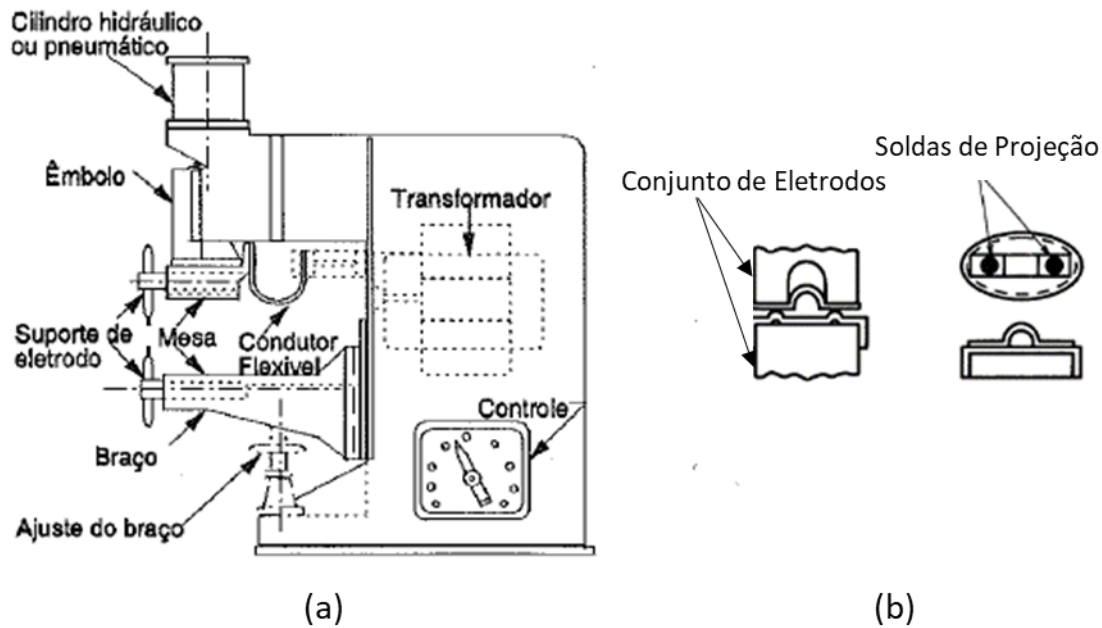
Representações esquemáticas: (a) equipamento de soldagem por projeção e (b) ponto de solda (adaptado de MARQUES, 2002)
